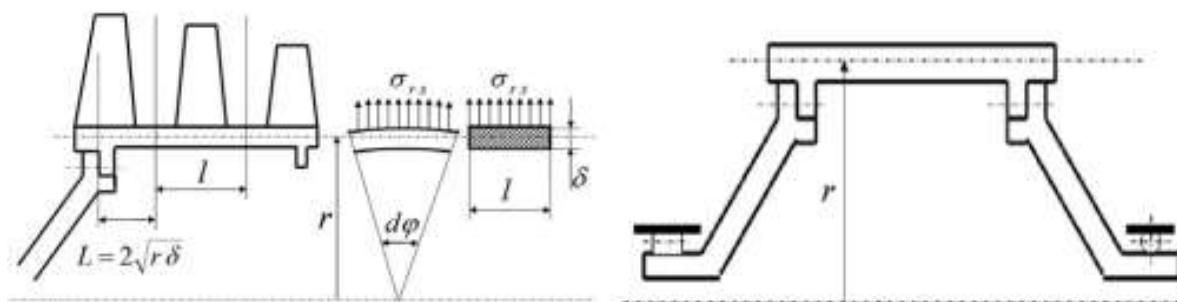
Розрахункова схема ротора барабанного типу
